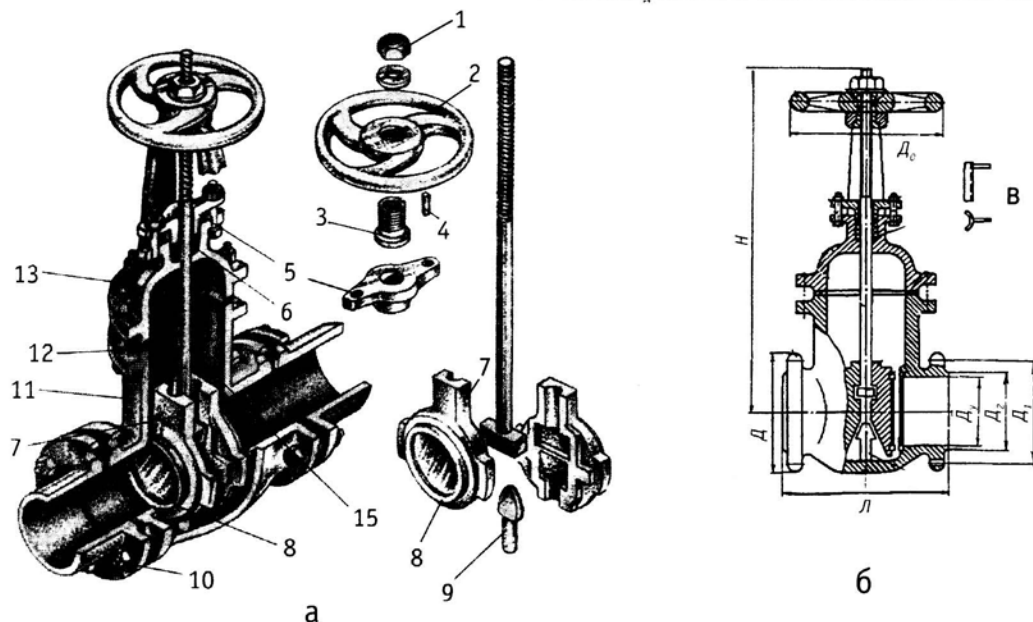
Задвижка параллельная из чугуна, фланцевая, с выдвижным шпинделем и ручным приводом: а — с маховиком на ходовой гайке, б — с маховиком на квадрате шпинделя, в — приспособление для набивки сальника;
